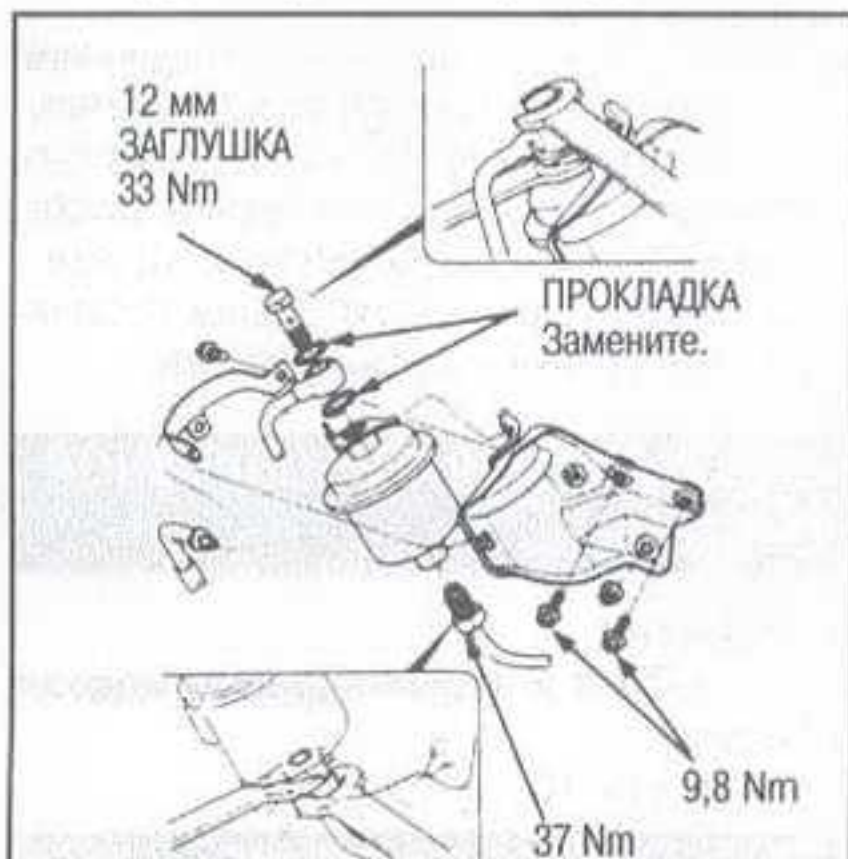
Топливный фильтр, устанавливаемый на теплоизоляционной перегородке и крепежный кронштейн в разобранном виде. На выходе фильтра (сверху) используется соединение с болтом типа «банджо», на входе — обжимное соединение
